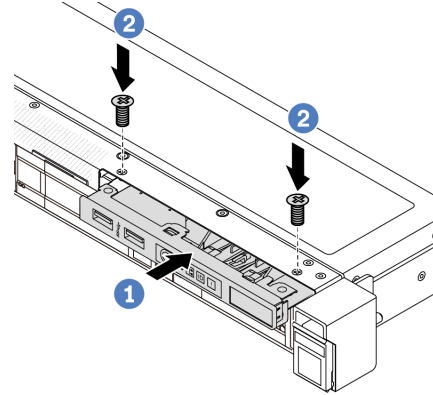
Instalar um módulo de E/S frontal no chassi de 3,5 pol.
